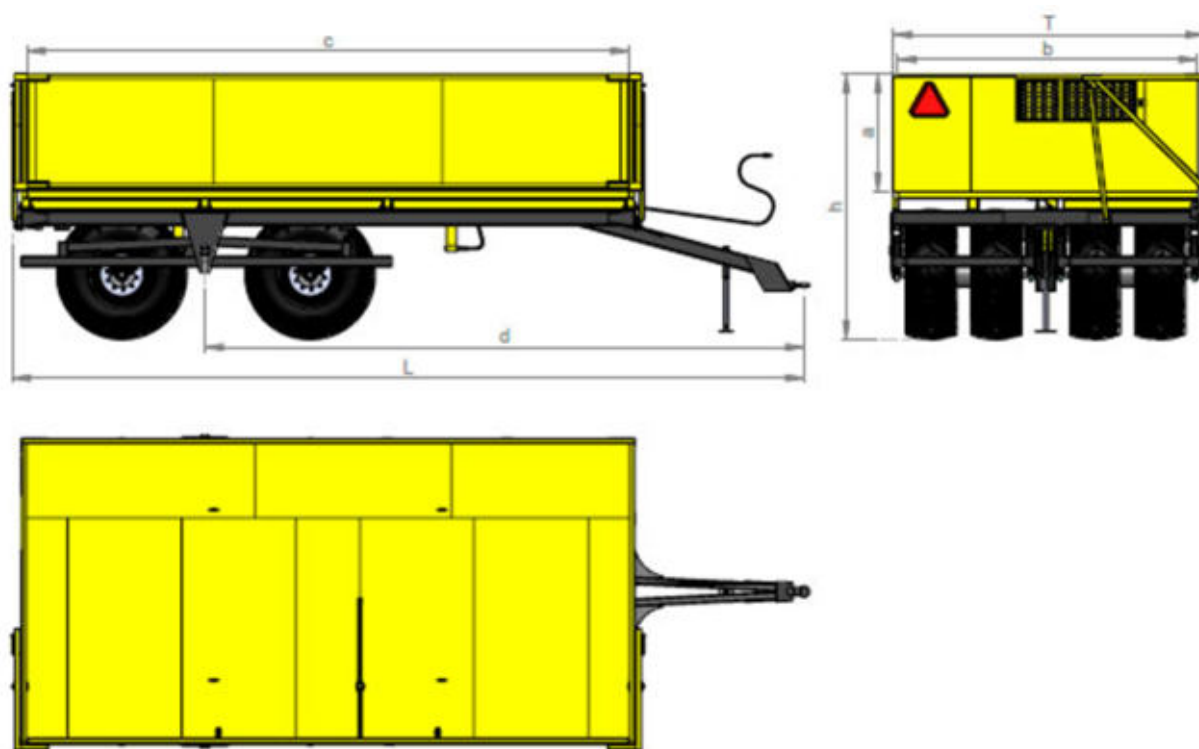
Основные размеры колесного полуприцепа TRL-30 F
